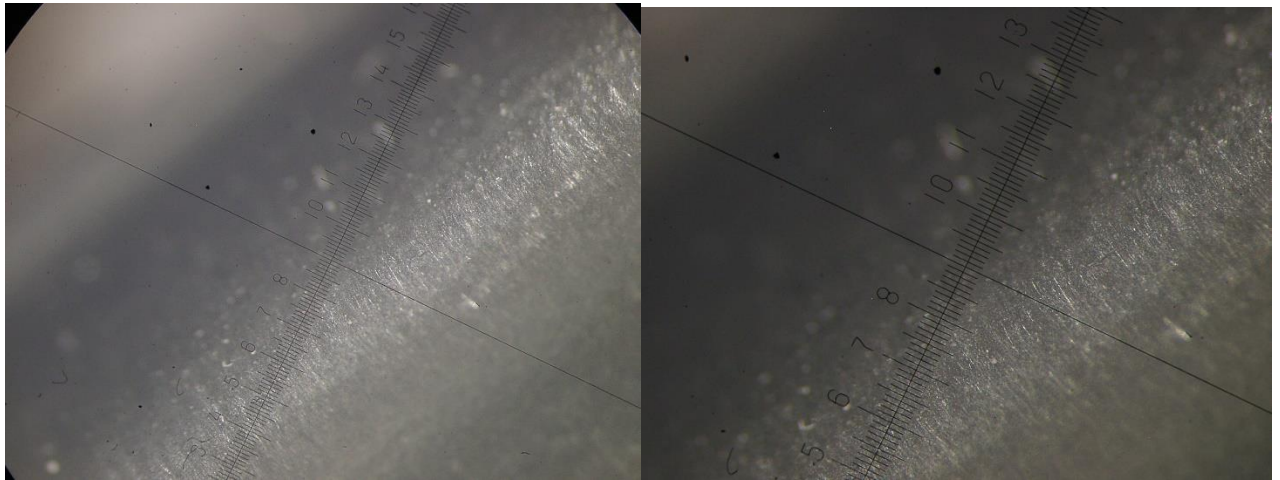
Зовнішній вигляд поверхні феромагнітного зразка зі сталі 40Х13
